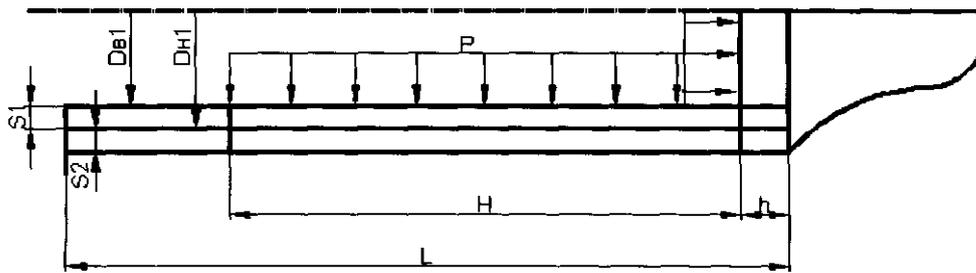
Схема плоской параметрической модели двухслойного гидроцилиндра гидростойки крепи М144
